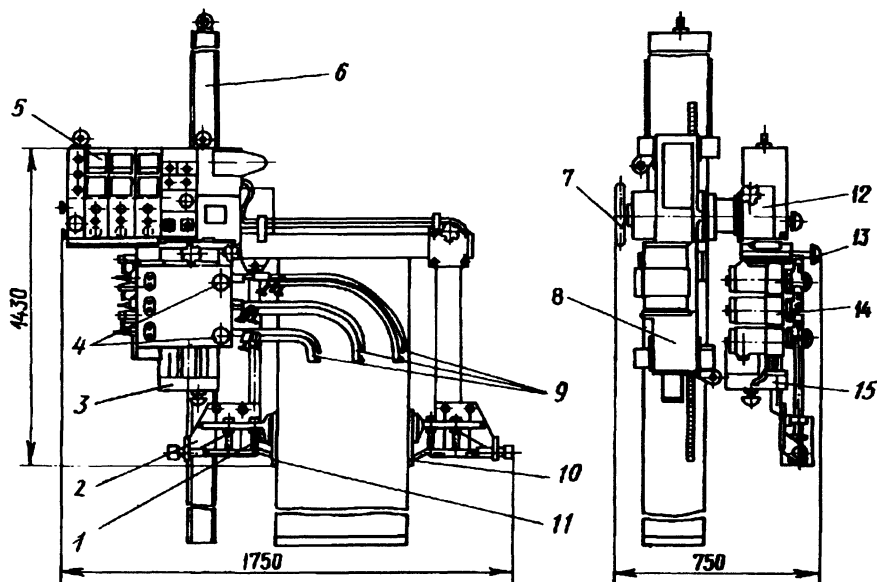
Автомат АШ112 для электрошлаковой сварки:
